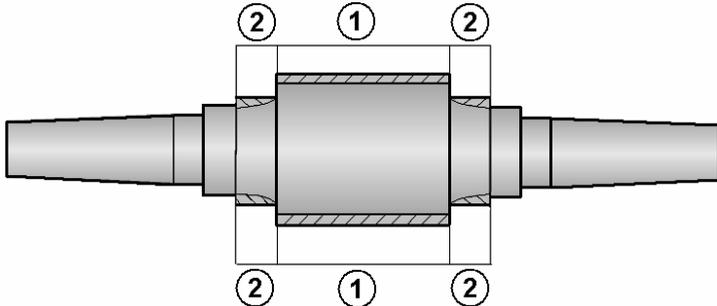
Схема удаления припуска с заготовки прокатного вала.
